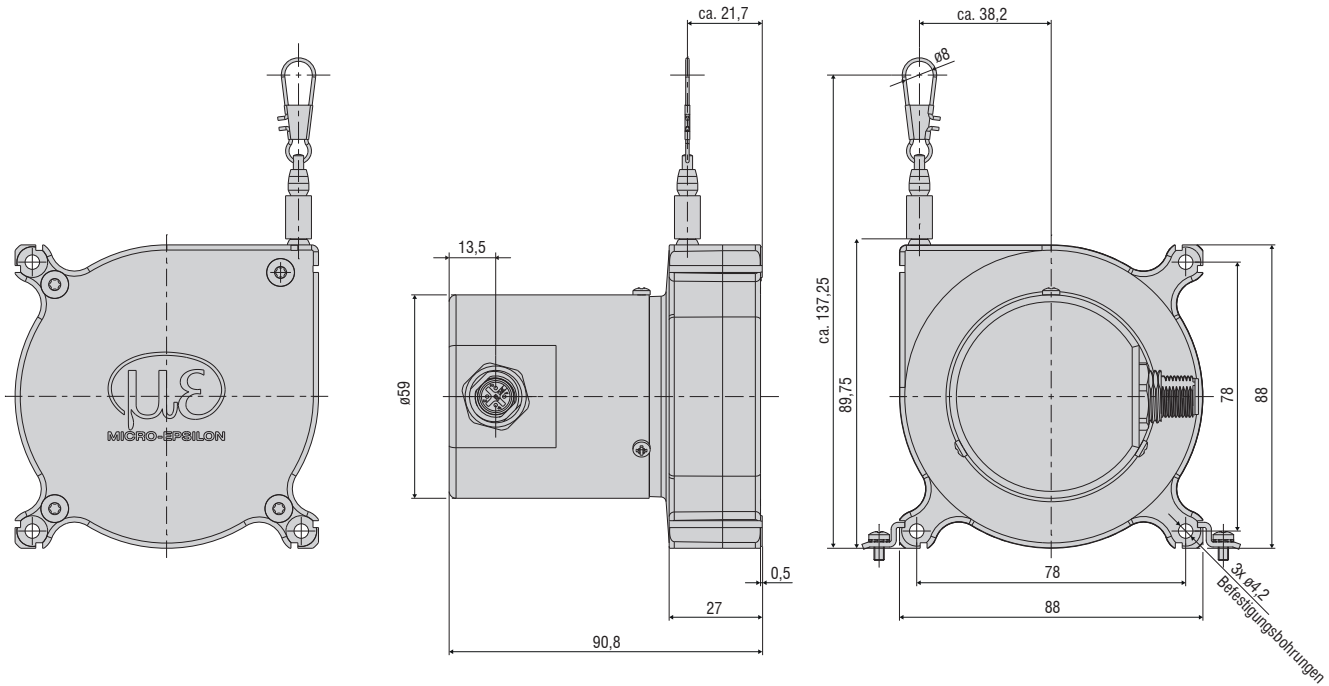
Maßzeichnung WPS-xxx-MK88-SR12-CO mit CANopen, Abmessungen in mm
